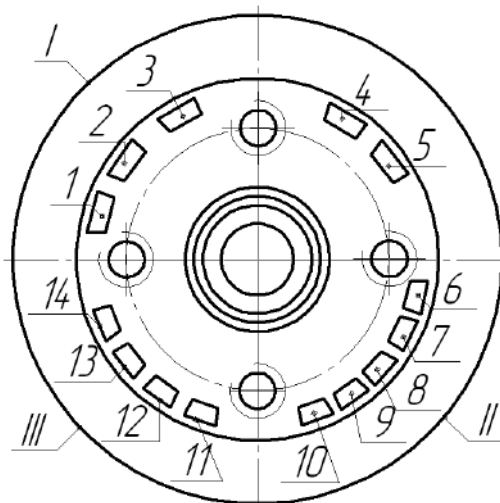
Знаки маркировки и клейма на правом торце оси колесной пары с подшипниками качения с торцовым креплением шайбой
